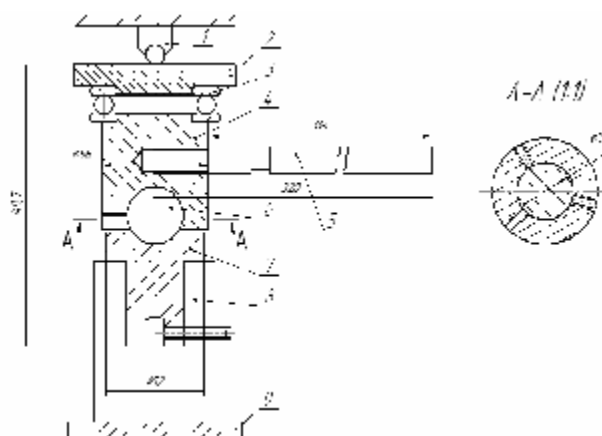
Схема приспособления установки к прессу Бринелля:
